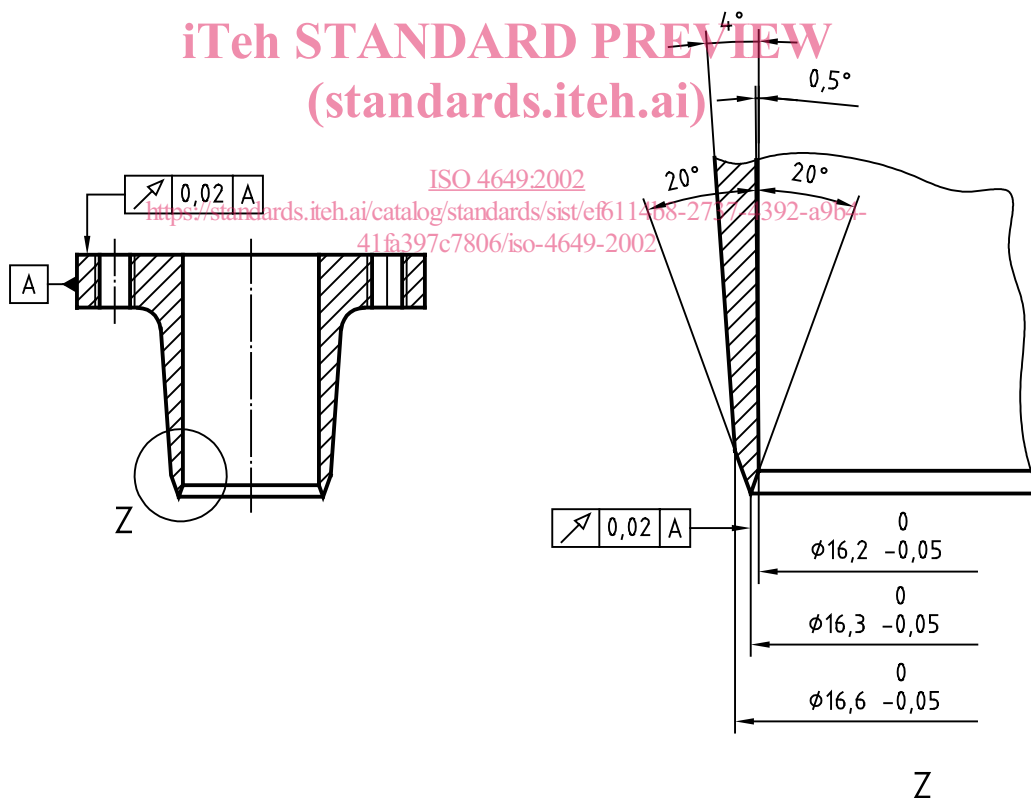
Exemple d'emporte-pièce rotatif pour préparation de l'éprouvette
